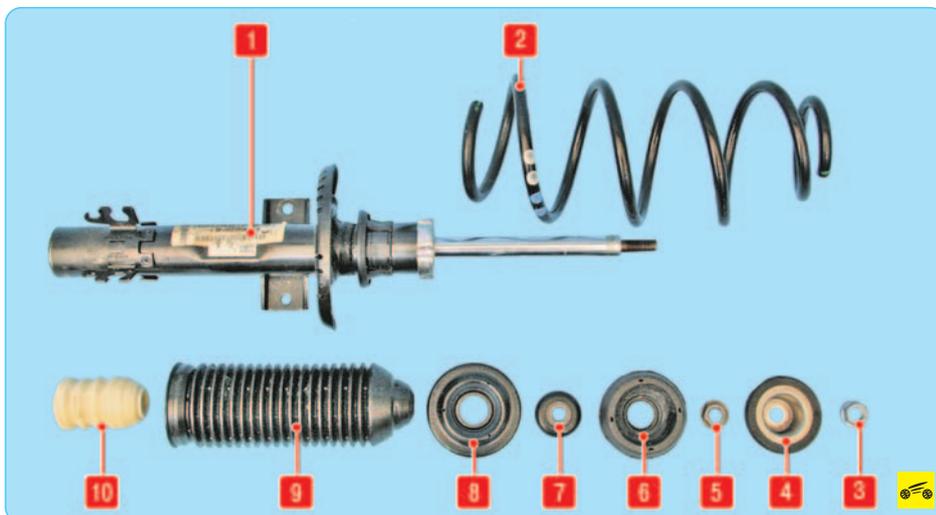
Детали амортизаторной стойки передней подвески: 1 – амортизатор; 2 – пружина; 3 – гайка верхнего крепления амортизаторной стойки; 4 – упор; 5 – гайка штока амортизаторной стойки; 6 – верхняя опора амортизаторной стойки; 7 – опорный подшипник; 8 – верхняя опорная чашка; 9 – защитный чехол; 10 – буфер сжатия
